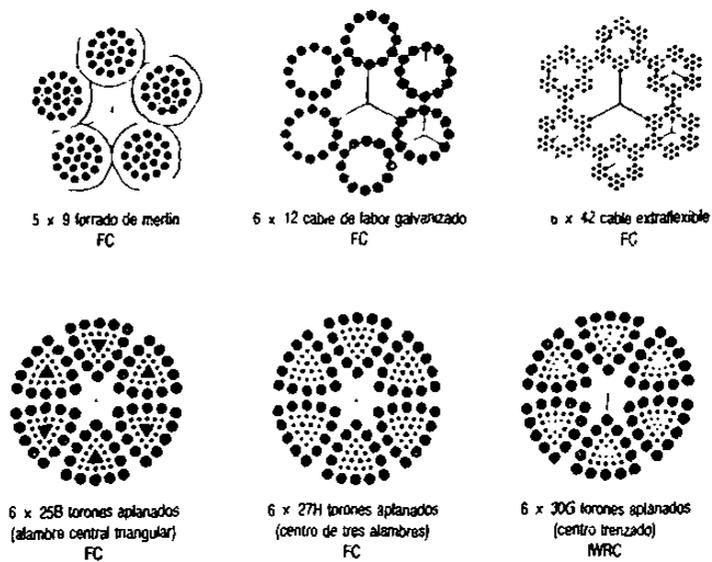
Secciones transversales de algunas construcciones especiales de cables Metálicos.
